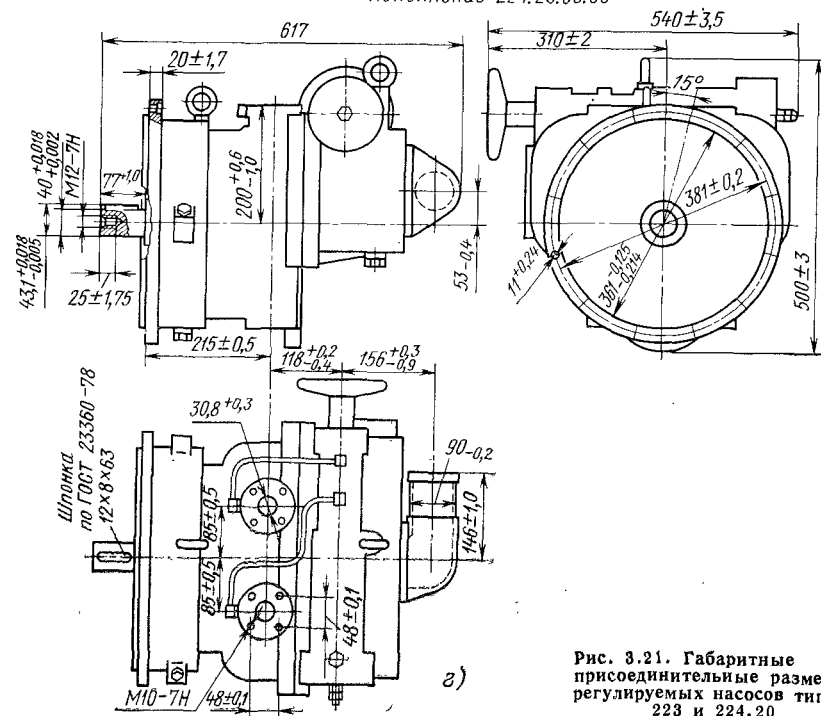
Габаритные и присоединительные размеры регулируемых насосов типов 223 и 224.20
